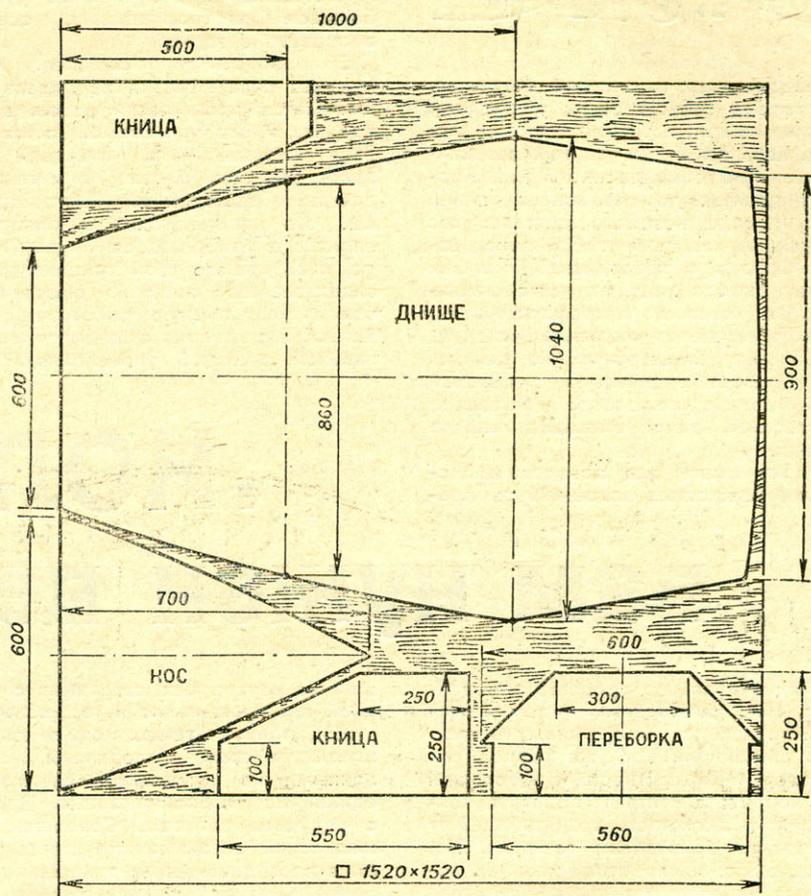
Заготовки элементов корпуса и схема их раскроя из листа фанеры.
